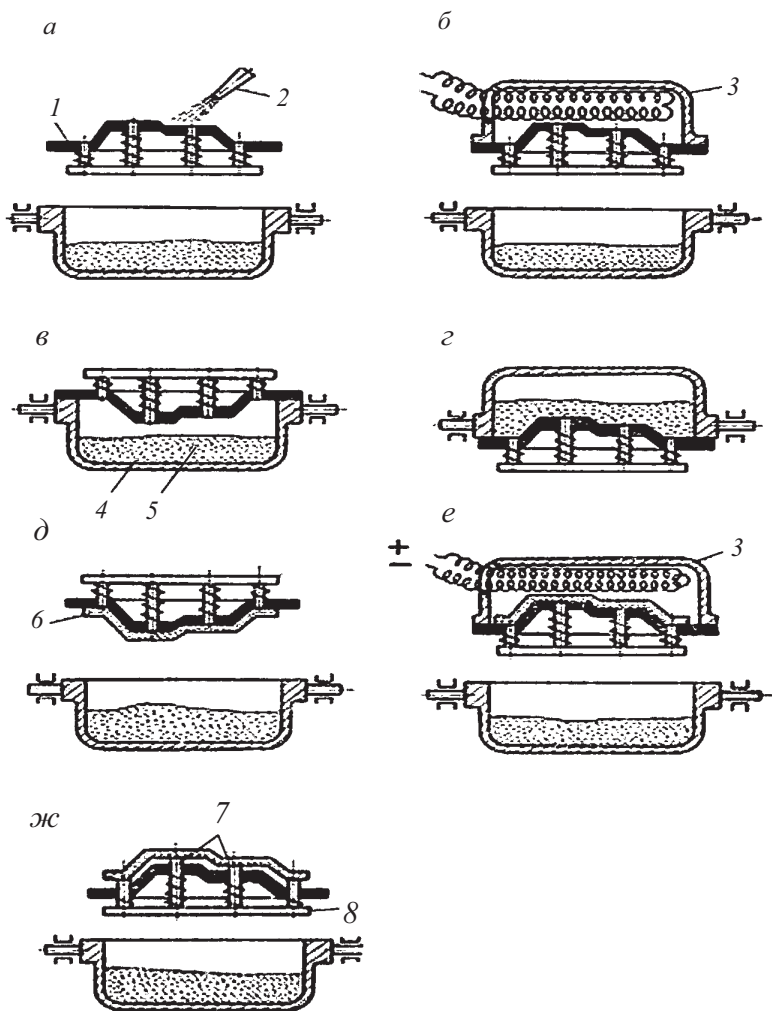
Схема процесса изготовления оболочковых полуформ:
